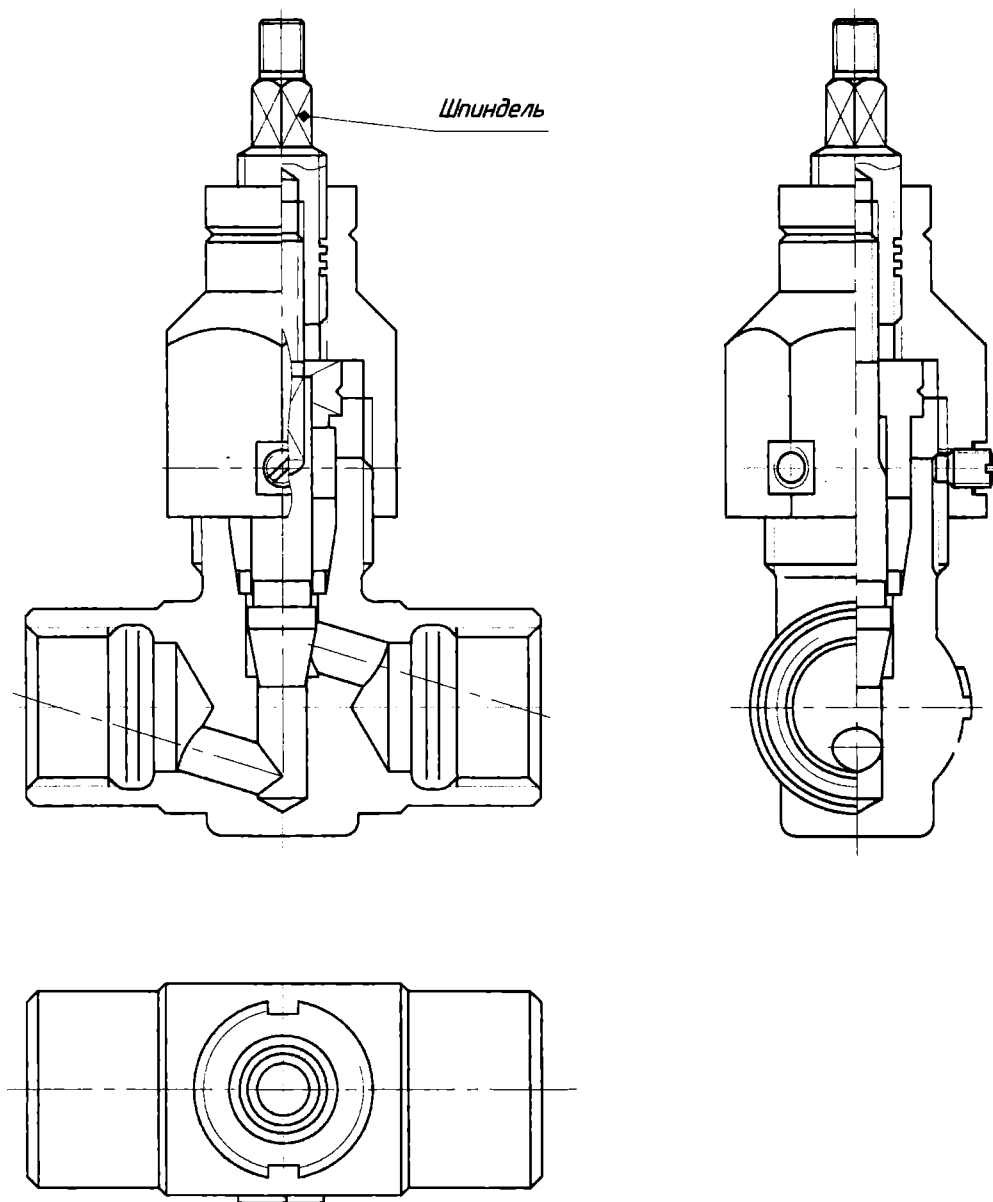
Установка шпинделя в сборе с клапаном и крышкой
